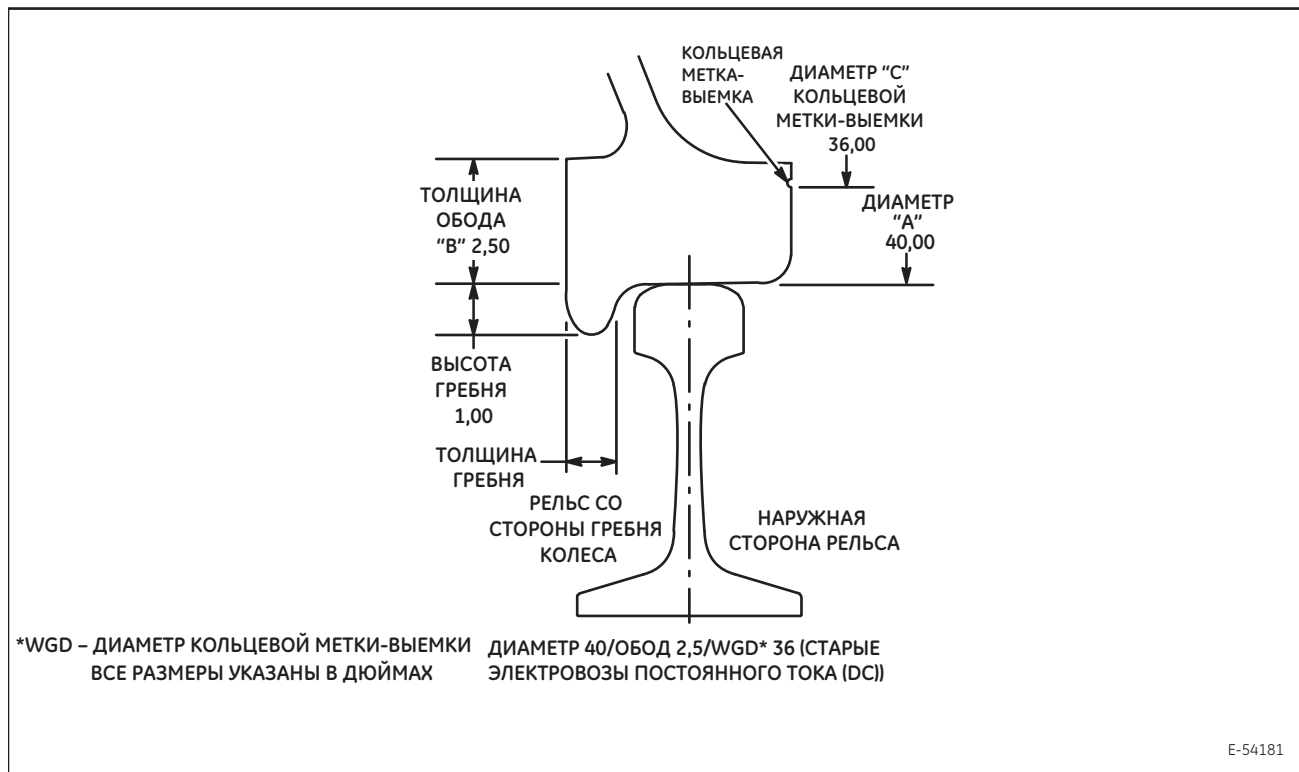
Размеры сопряжения колес с рельсами для 40-дюймовых колес.
